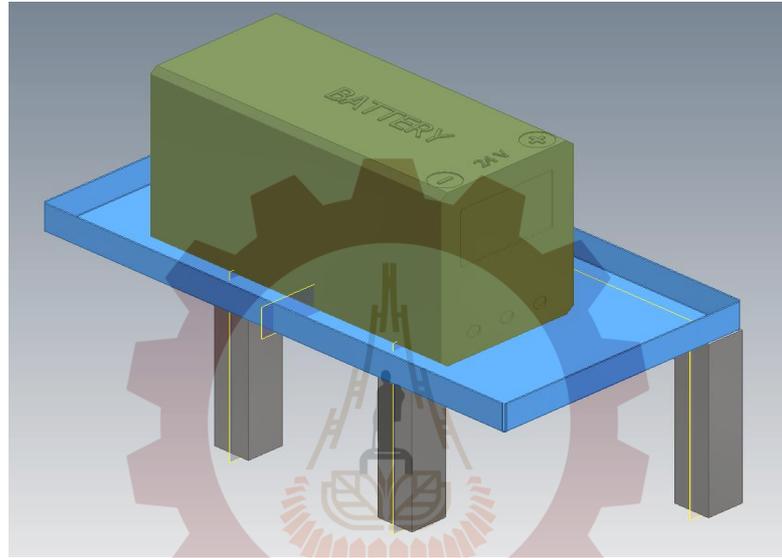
ASSY CONERSION KIT DRIVE CLEAN
